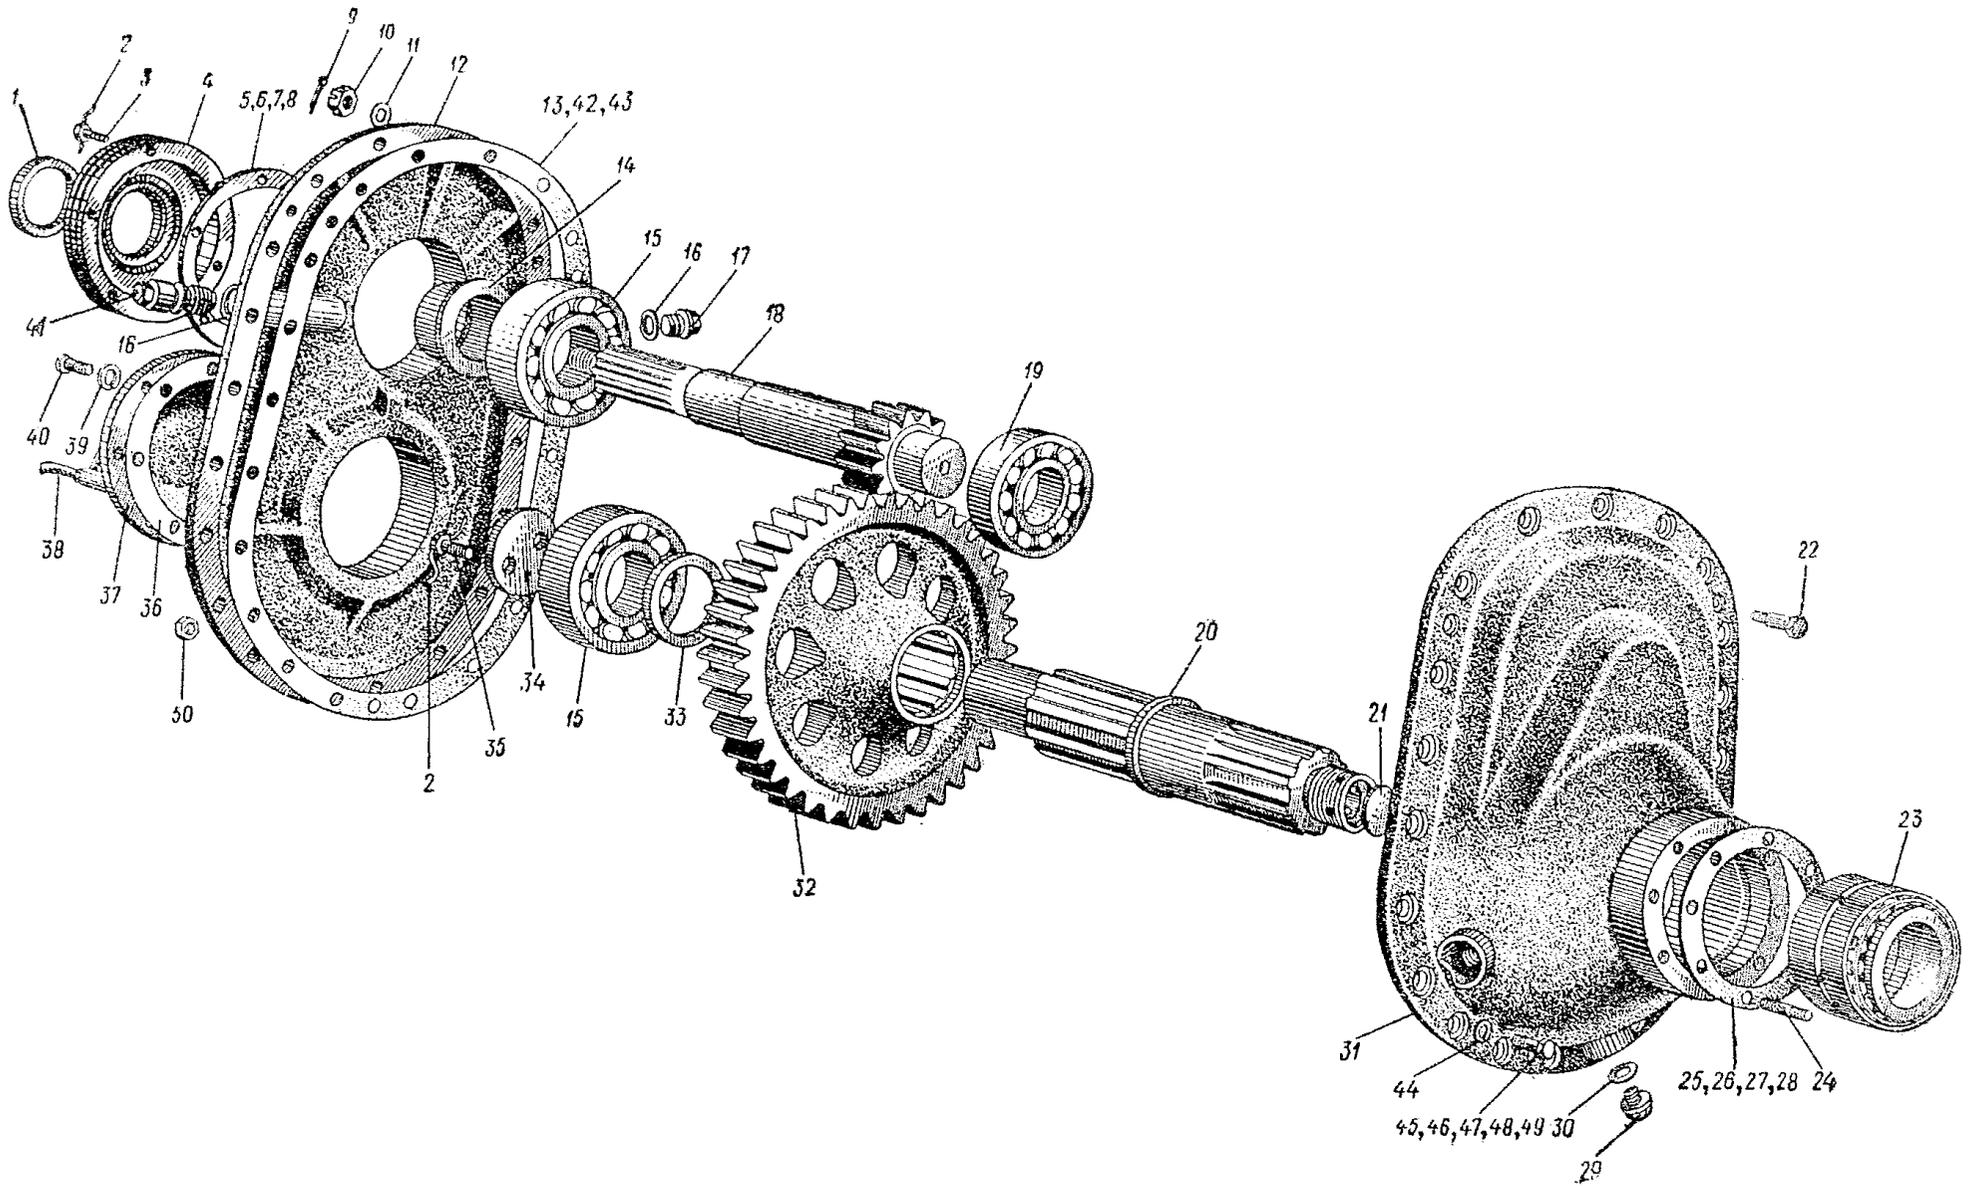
Узлы и детали бортовой передачи (лист 1)
